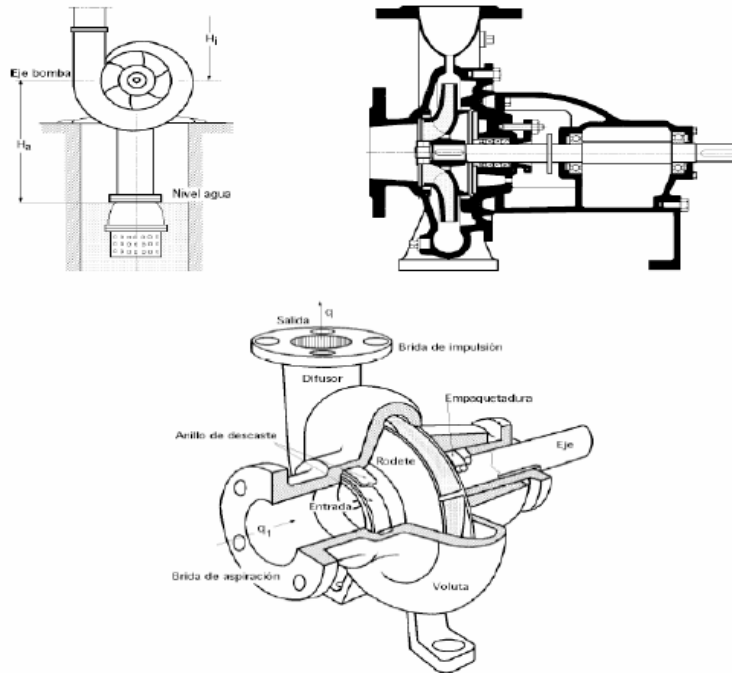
Bomba Centrífuga, Disposición, Esquema Y Partes. [1.1]
